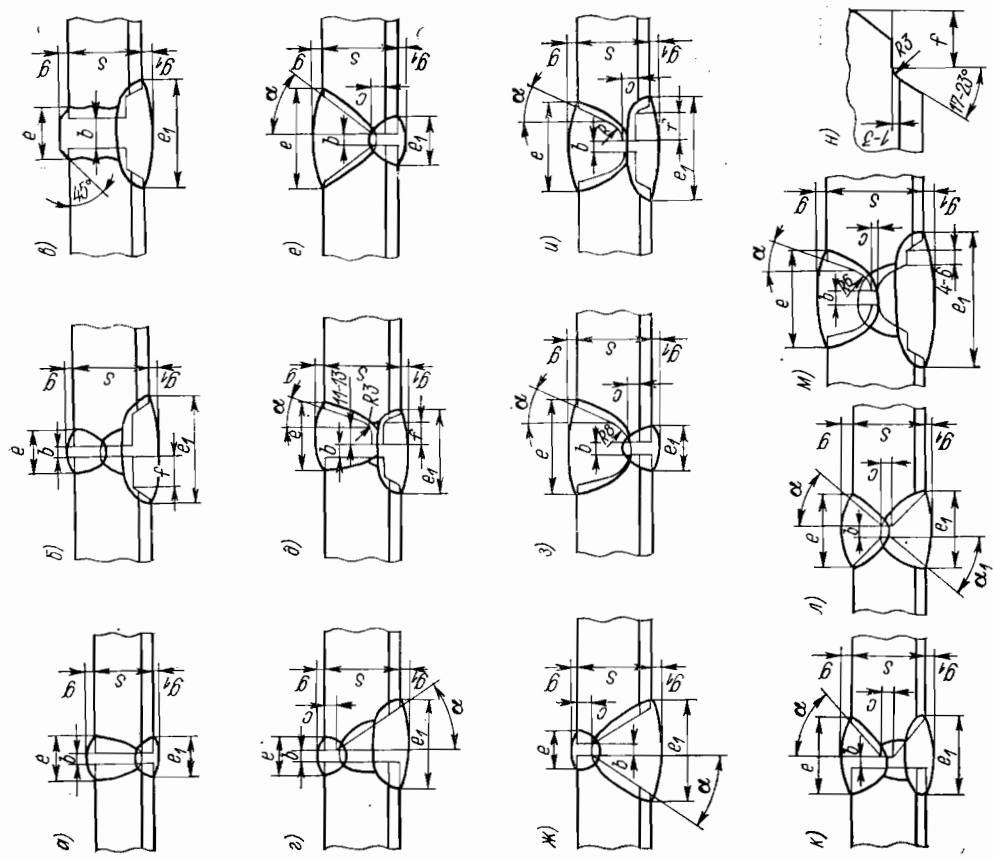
Конструкции стыковых сварных соединений двуслойной стали: а — двусторонние без скоса кромок; б, в — двусторонние без скоса кромок со снятием плакированного слоя; г — двусторонние со скосом одной кромки; д — двусторонние с криволинейным скосом одной кромки и снятием плакированного слоя; е, ж — двусторонние со скосом двух кромок; з — двусторонние с криволинейным скосом двух кромок; и — двусторонние с криволинейными скосами двух кромок и снятием плакированного слоя; к — двусторонние с двумя скосами одной кромки; л — двусторонние с двумя скосами двух кромок; м — двусторонние с двумя криволинейными скосами двух кромок и снятием плакированного слоя; н — элемент снятия плакированного слоя
